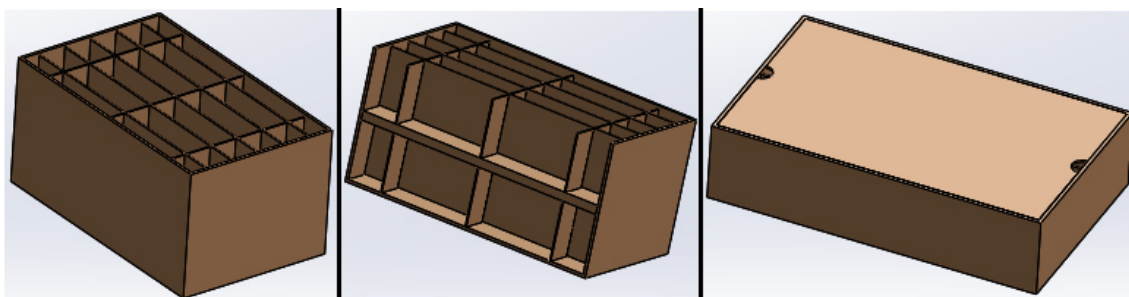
Modelação 3D da nova proposta para a embalagem do cliente D– Embalagem completa, corte de plano frontal e corte de plano vertical
